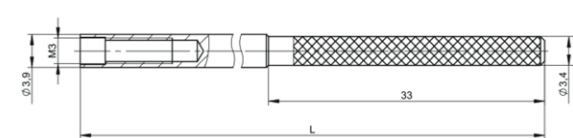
Ausziehwerkzeug für Typ 6405 Typ 1349...
